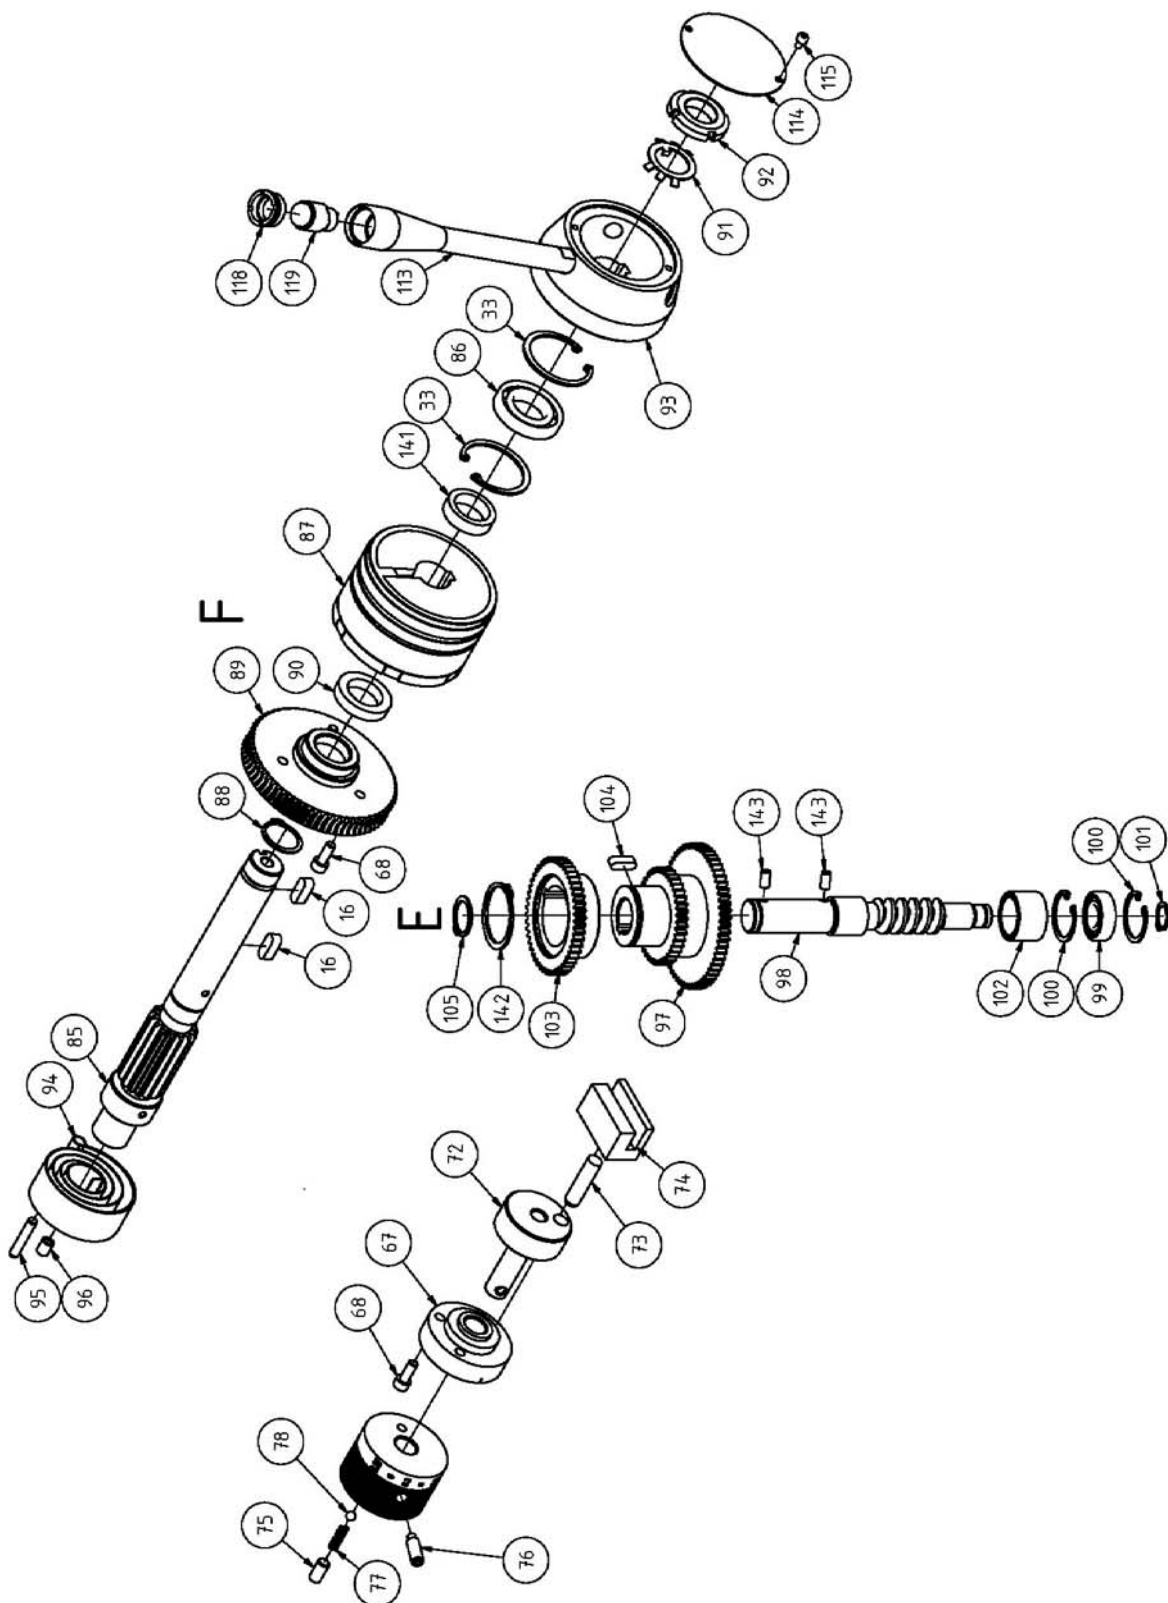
Bohrkopf 5 von 6- Cabezal taladrador 5 de 6
